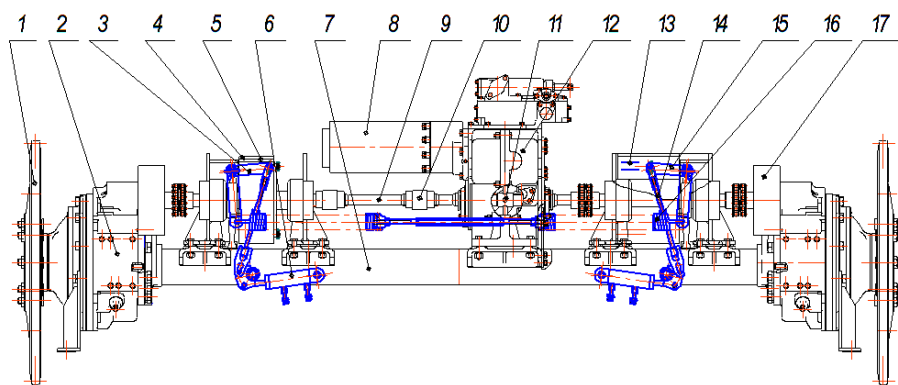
Мост ведущий уборочной гусеничной машины (вид сверху):
